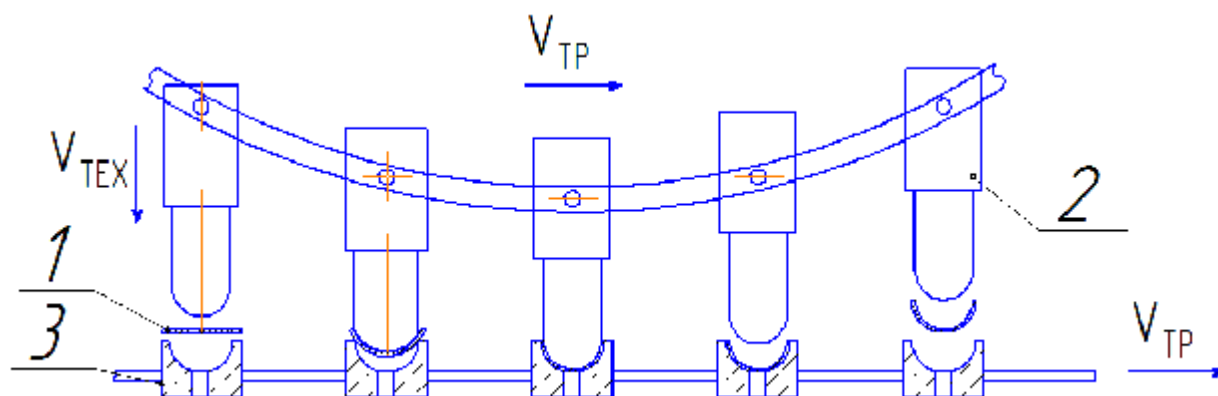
Машины 3 класса: 1 – заготовка; 2 – инструмент; 3 – изделие.
